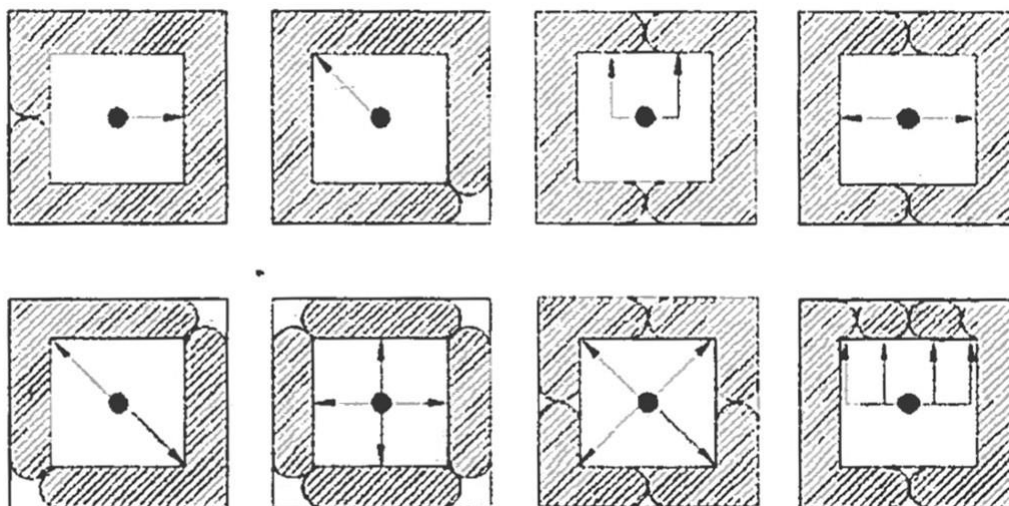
Alterações das linhas de soldadura [8].
